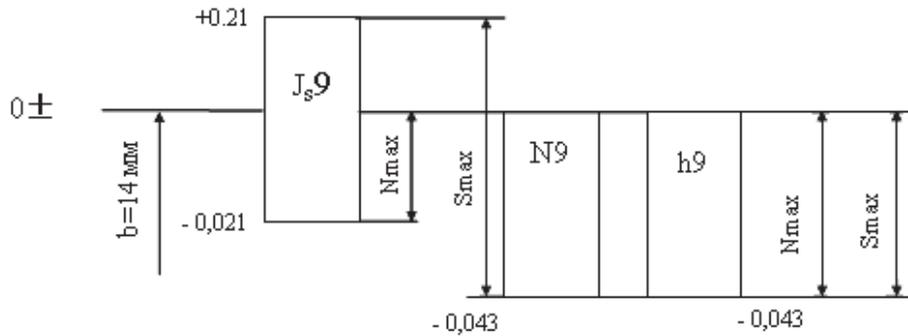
Схема расположения полей допусков деталей шпоночного соединения
